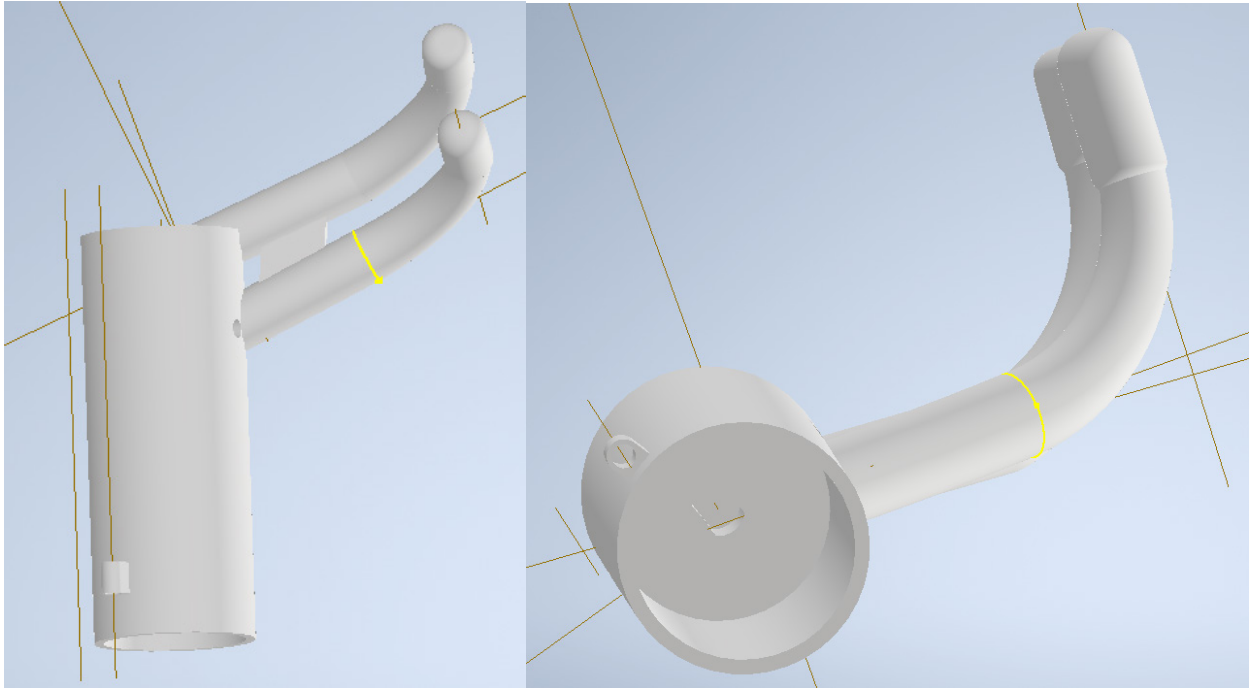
Unión del ensamblaje de los dedos con la pieza enganchada al husillo.
